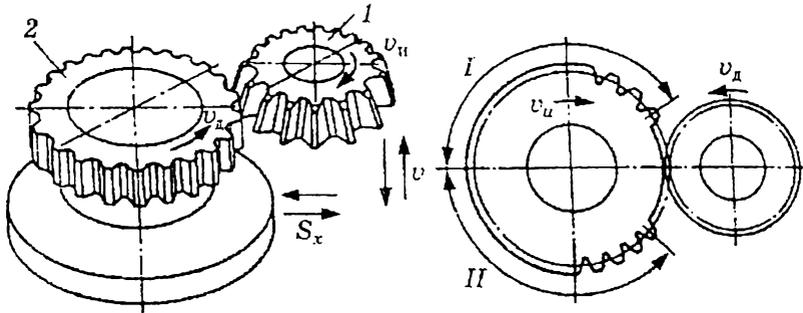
Схема нарезания зубьев зубодолблением круглым долбяком:
